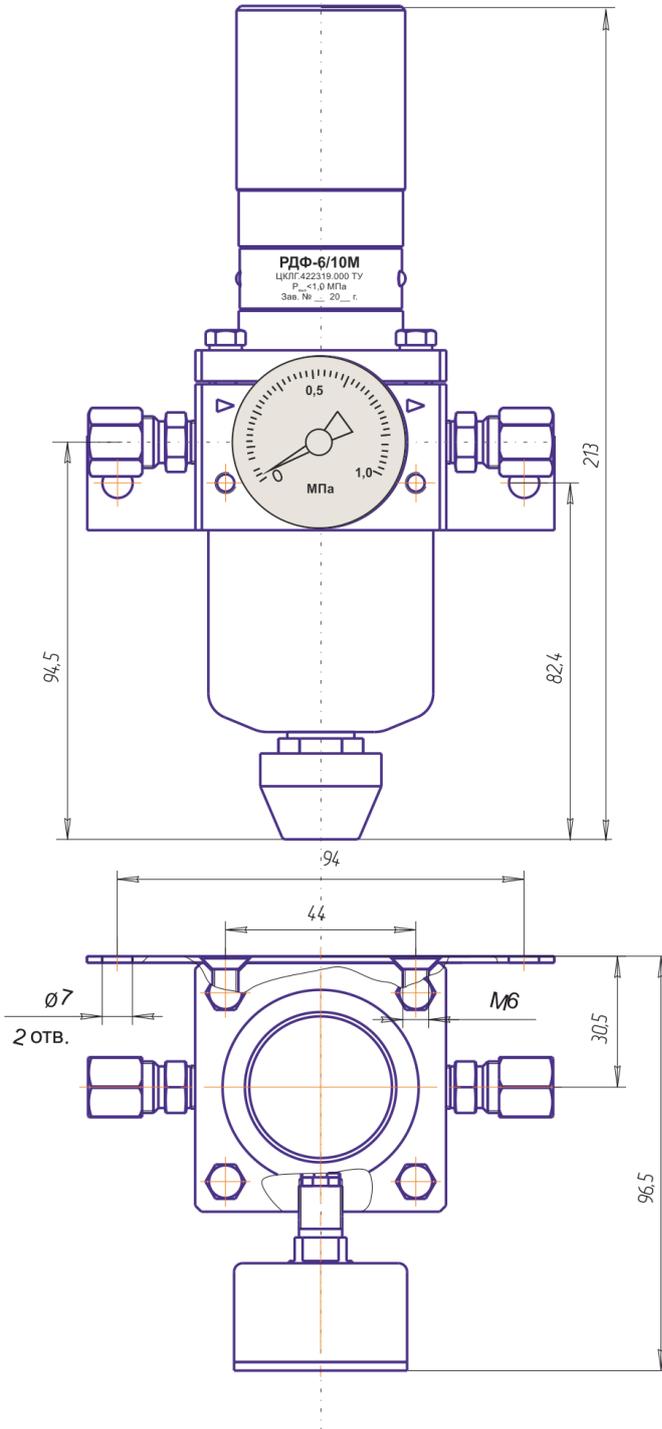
Габаритные и присоединительные размеры редуктора РДФ-6/10М
